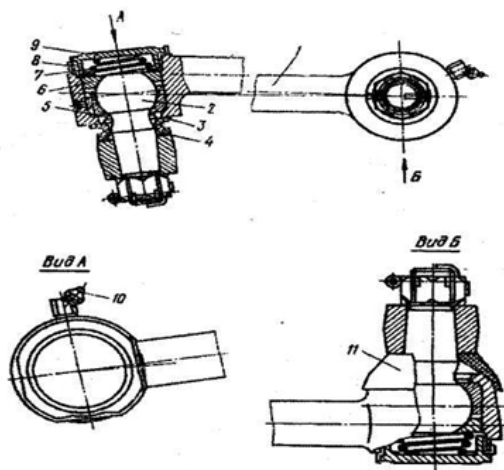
Продольная рулевая тяга: 1-стержень тяга; 2-шаровой палец; 3-защитная накладка; 4-обойма накладки; 5,6-вкладыши; 7-пружина; 8-стопорная шайба; 9-крышка; 10-масленка; 11-защитная накладка
